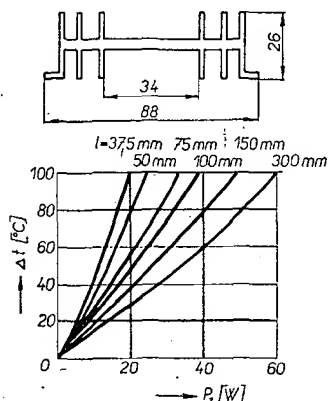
Profil č. 754, stejné údaje jako u obr. 13
